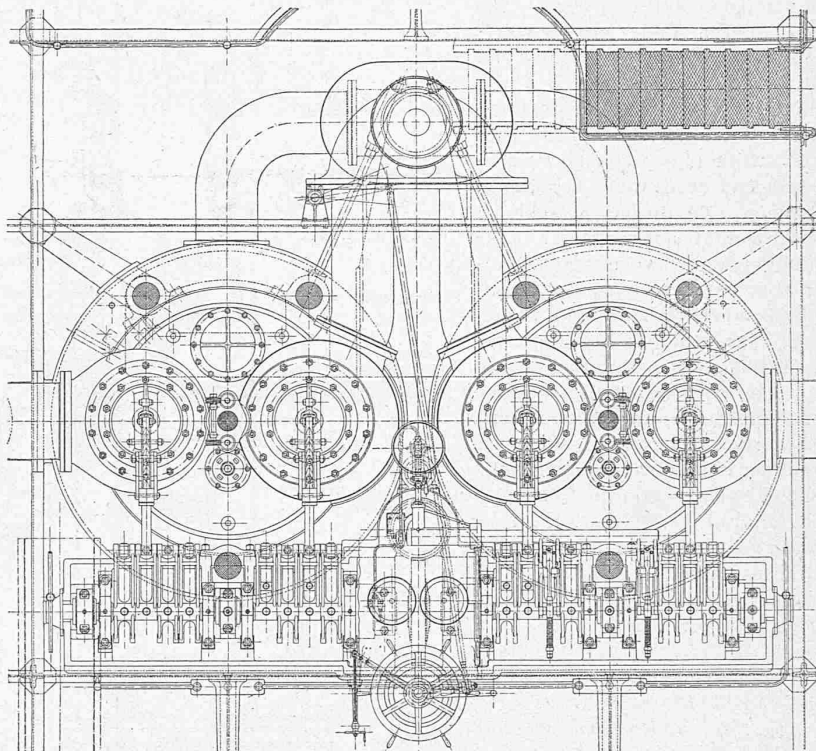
Grundriss (Schnitt zwischen den Cylindern) 1:50.
